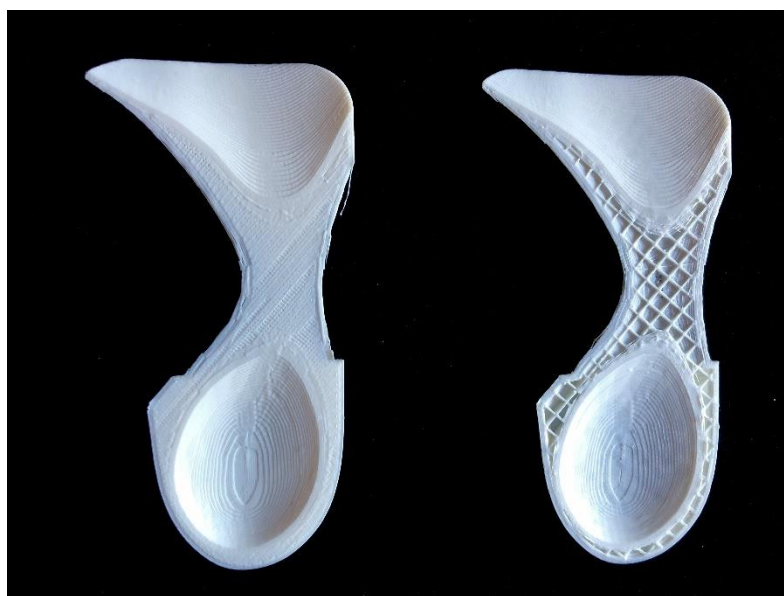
A sinistra si vede la struttura interna di un ortesi plantare stampata con un riempimento “infill” al 75%, a destra si può osservare la stessa ortesi ma stampata con un riempimento al 25%
